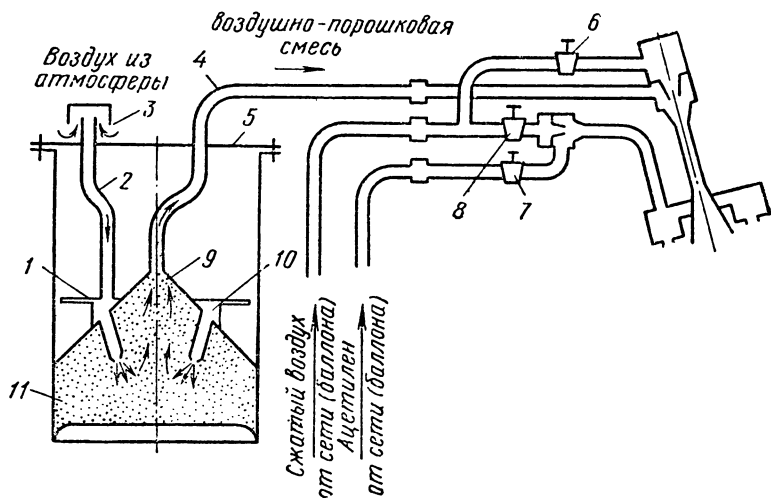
Схема установки порошкового напыления УПН-6-63:
